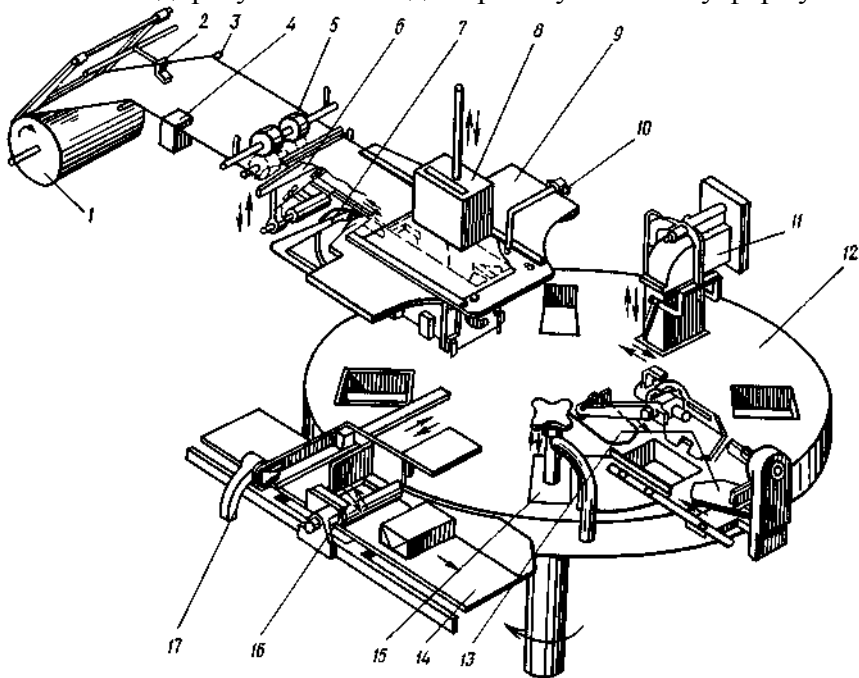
Схема утворення пакета автомата АРІС: 1 - рулон; 2 - механізм притискування; 3 - направляючий валик; 4 - дататор; 5 - регульовані сектори; 6 - ножі; 7 - важелі; 8 - пуансон; 9 - формуюча матриця; 10 - шуп; 11 - дозатор; 12 - формуючий стіл; 13 - механізм закладення; 14 - транспортер; 15 - механізм підпресування; 16 - перевертач; 17 - знімач пакетів
